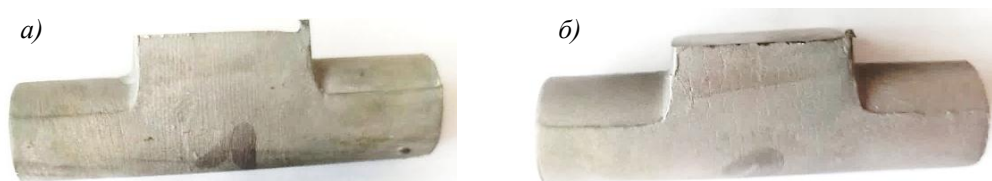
Литые заготовки из сплавов ВЖЛ220 (а) и ВЖЛ718 (б)
